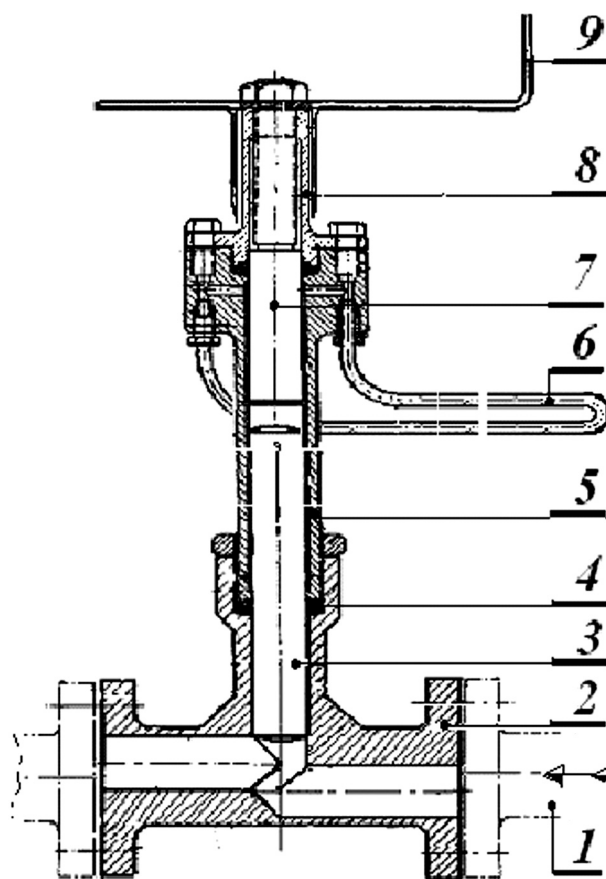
Манометрический автостабилизатор температуры сушильного агента с нестандартным корпусом: 1 – паропровод; 2 – корпус исполнительного органа; 3 – плунжер; 4 – сальник; 5 – гидроцилиндр; 6 – термодатчик; 7 – настроечный шток; 8 – головка; 9 – ручка
